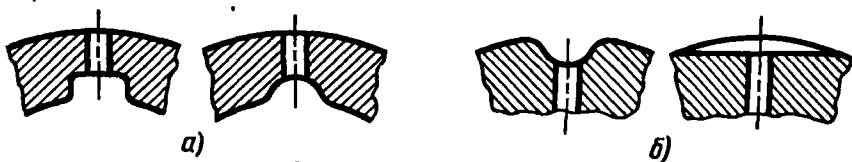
Смазочные канавки в подшипниках (а) и на валах (б)
